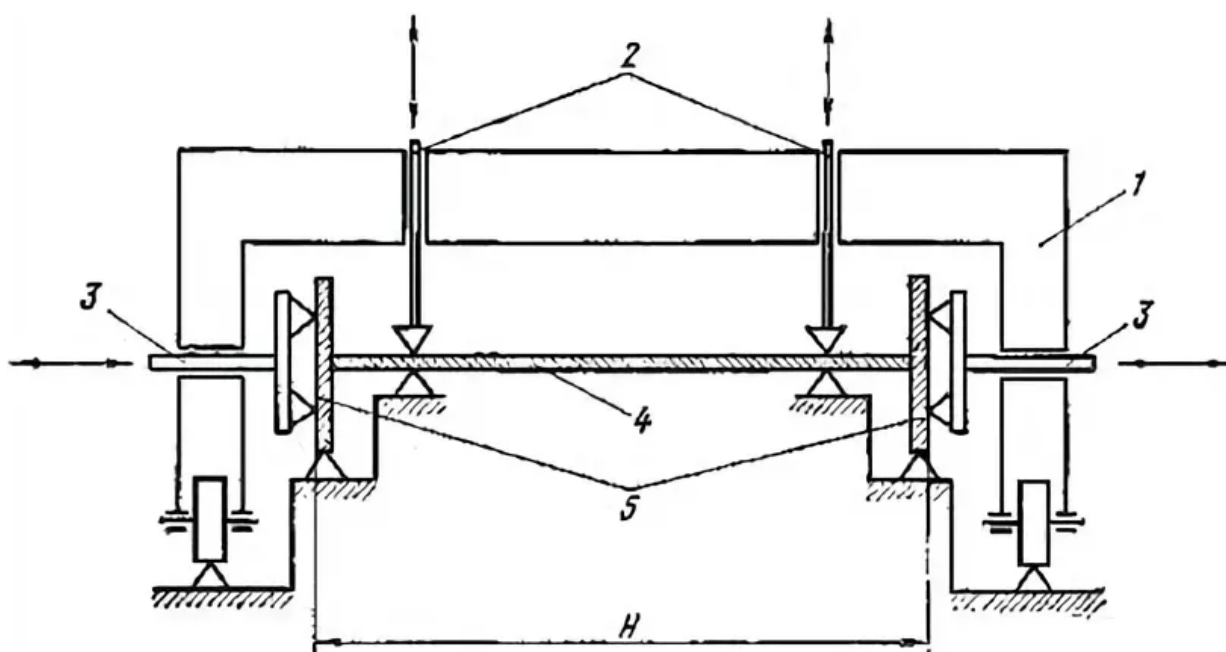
Схема самоходного портала для сборки двутавровой балки:
